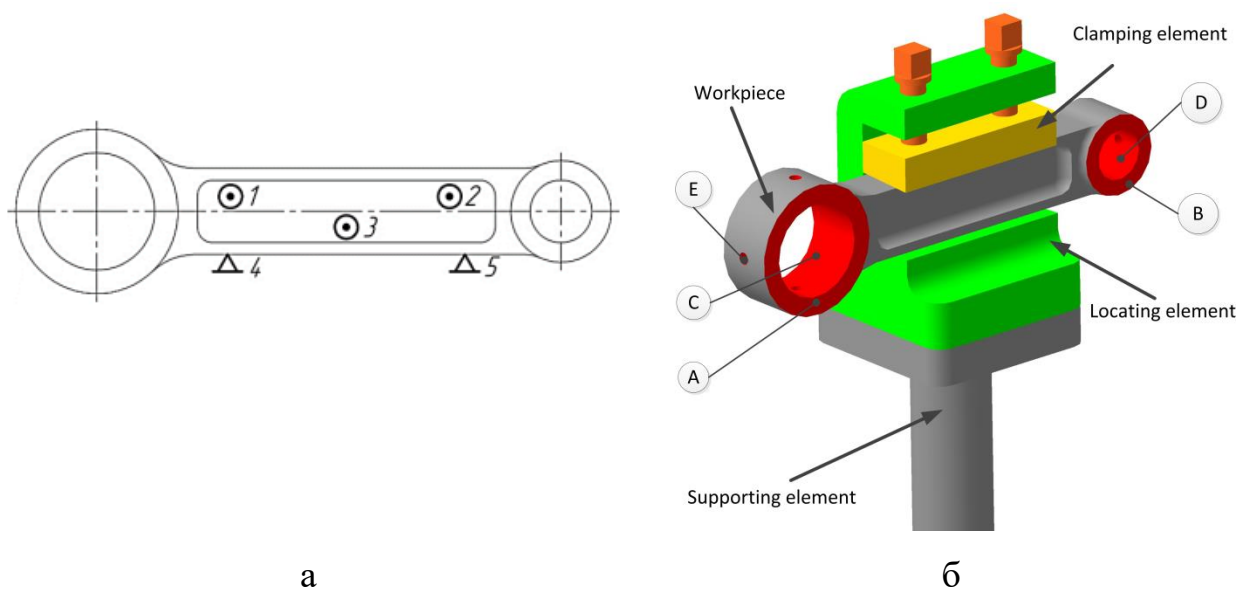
Гнучкий ВП для оброблення нерознімного шатуна з оброблюваними поверхнями на комплексній операції з ЧПК [36]: а – схема базування; б – 3D візуалізація
